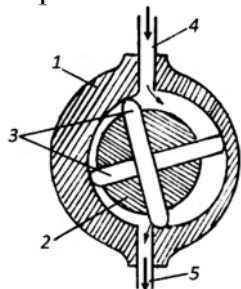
Pompa de transfer: 1 – inel (stator); 2 – rotor; 3 – palete; 4 – orificiu de aspirație; 5 – orificiu de refulare
